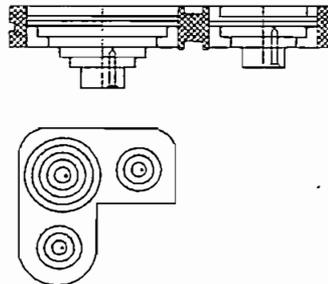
Boquillas para el Ingreso de Cables al Armario
